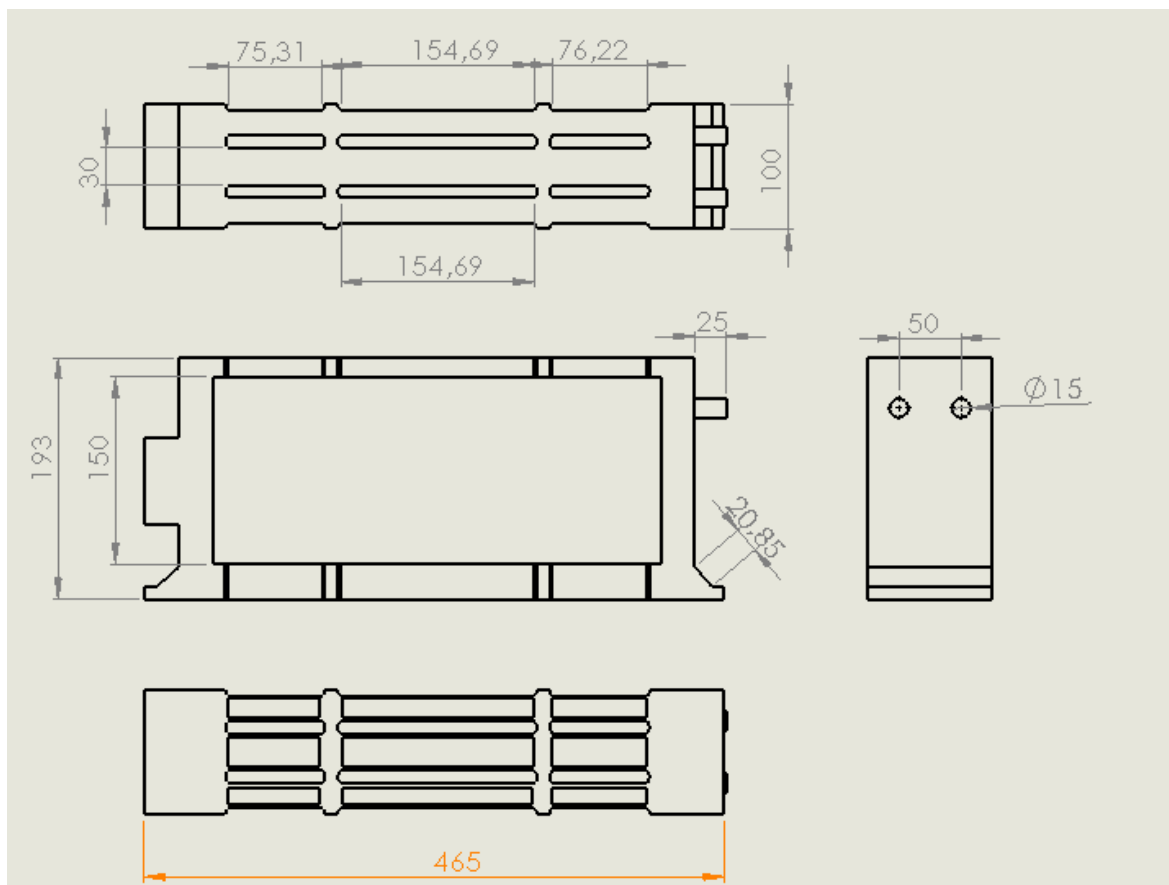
Vistas y dimensionamiento Renault Twizy (mm)
